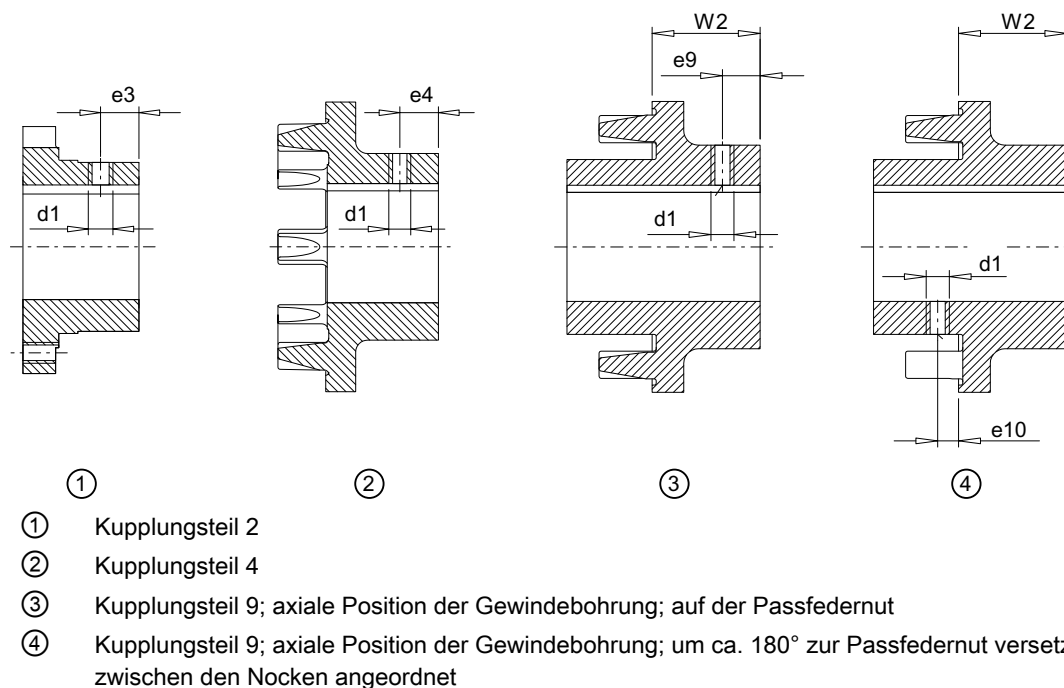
Durchmesser und axiale Position der Gewindebohrung auf der Nabe
